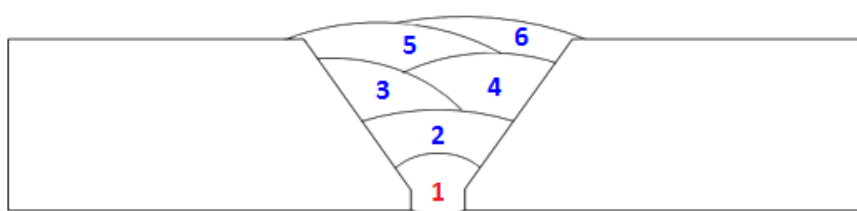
Esquema da junta soldada indicando as camadas e os passes de soldagem.
